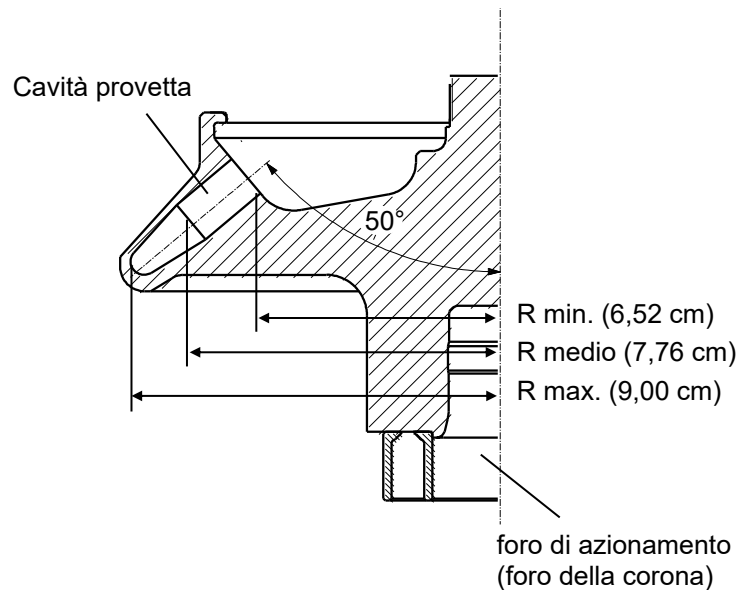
Vista a sezione trasversale di rotore P50A3
